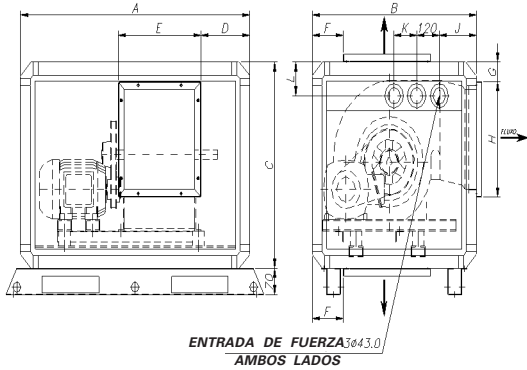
Dimensiones Módulo Ventilador 350 a 500
